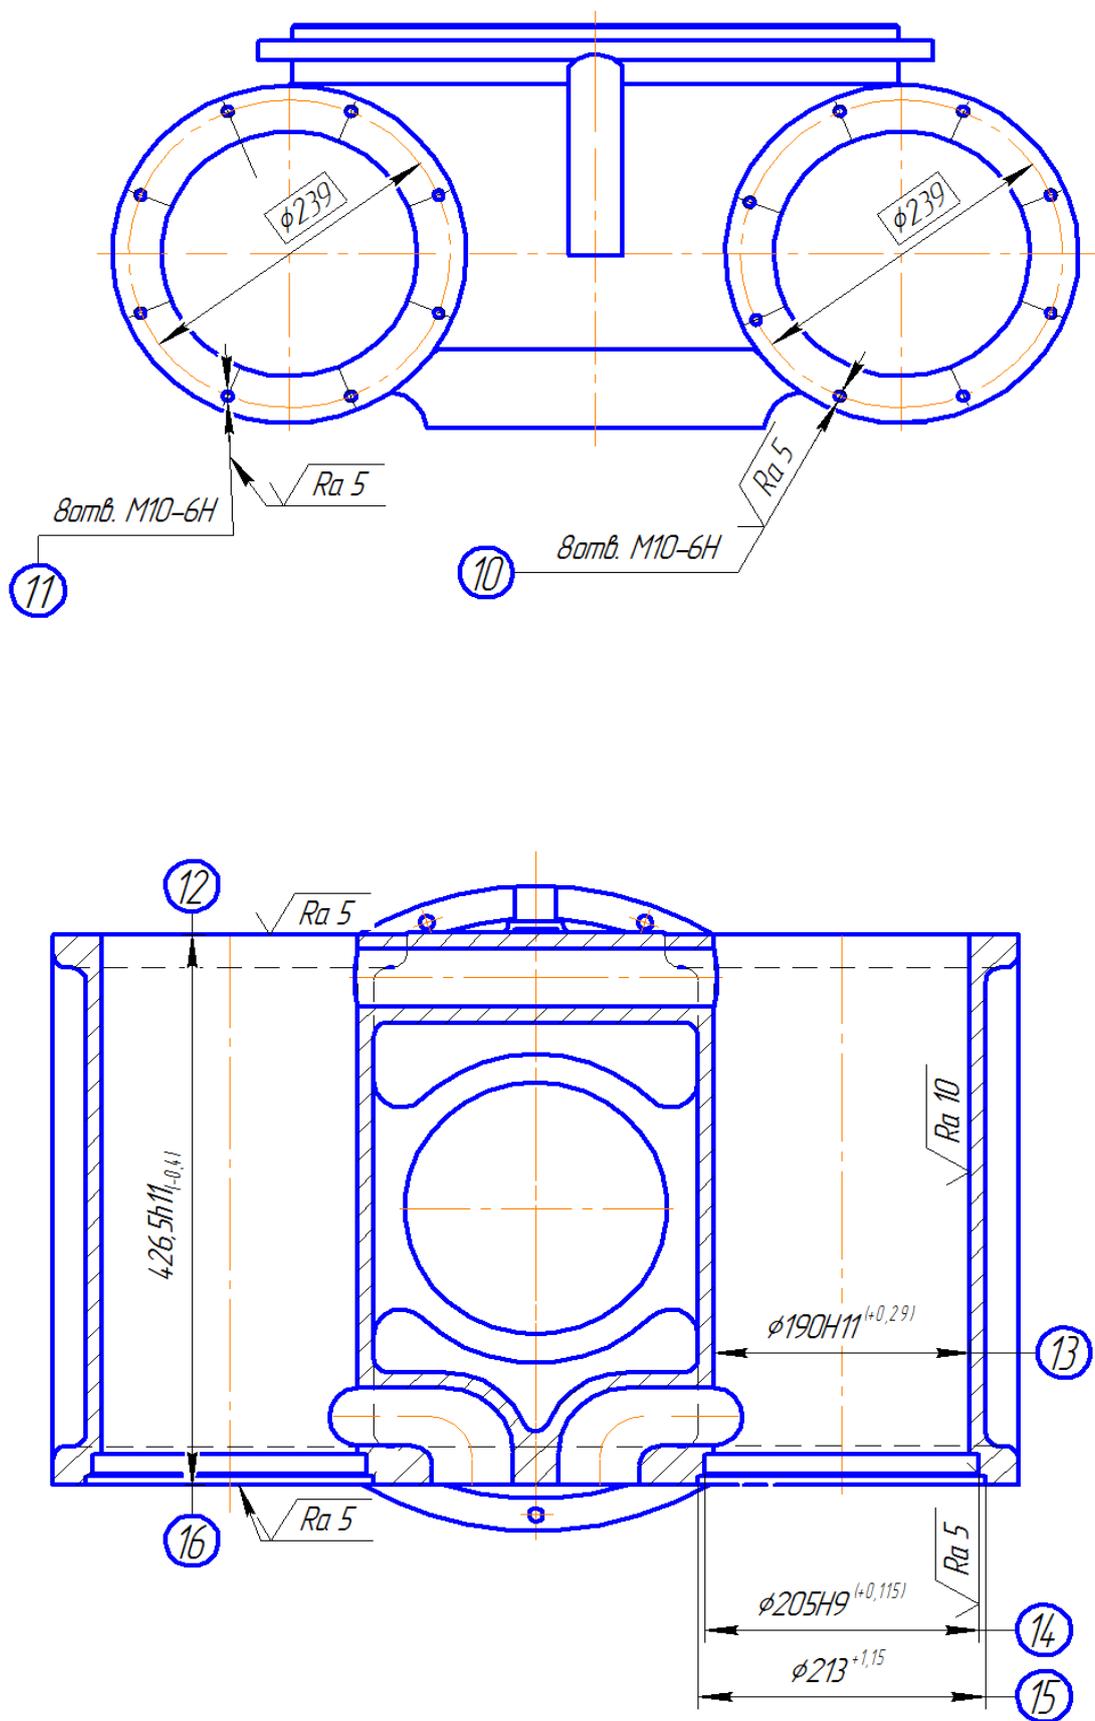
Эскиз детали «Корпус привода вентилятора» (сечение Б-Б)
